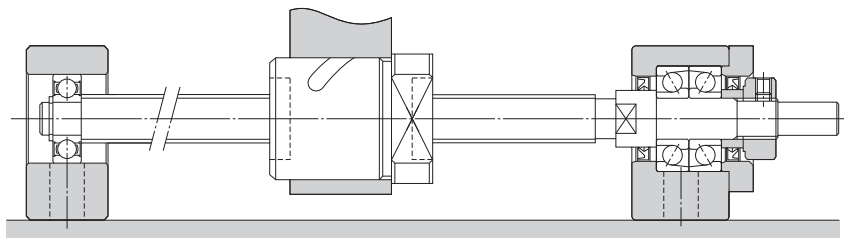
Пример установки концевой подшипниковой опоры прямоугольного типа
